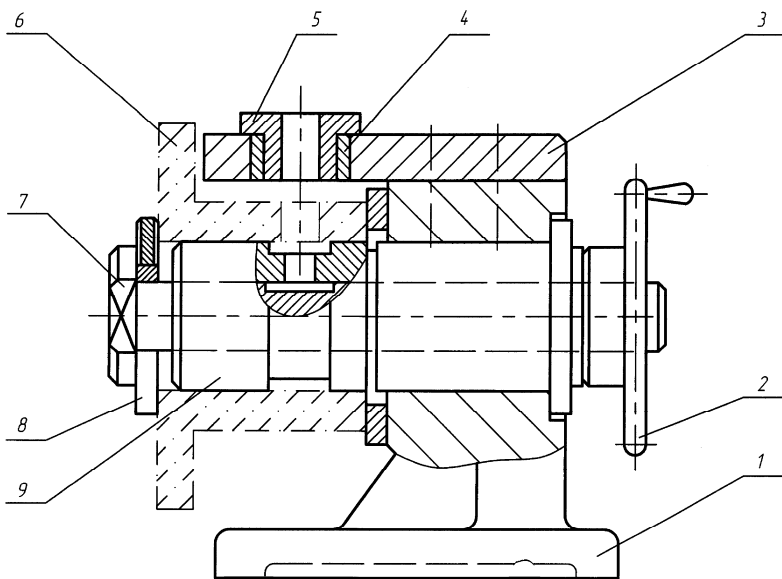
Специальное приспособление для сверления отверстия во втулке:
